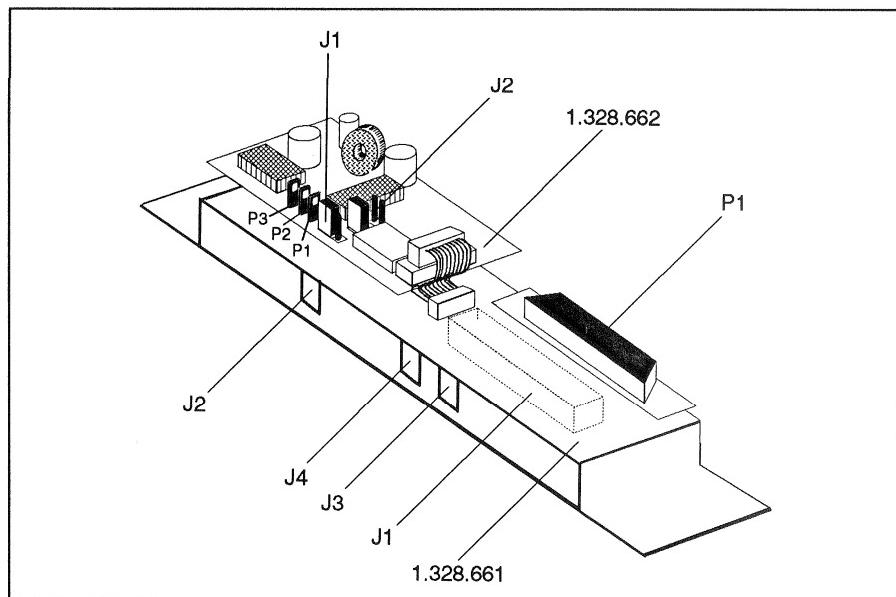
Jumper und Anschlüsse der parallelen Fernbedienung
